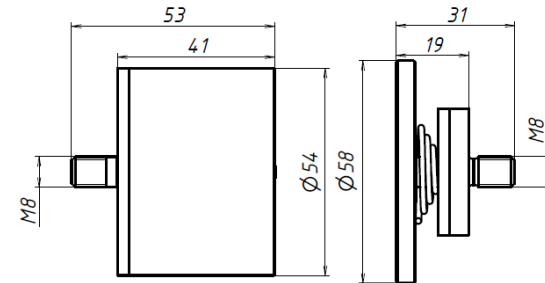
Габариты корпуса и якоря замка AL-70FC
